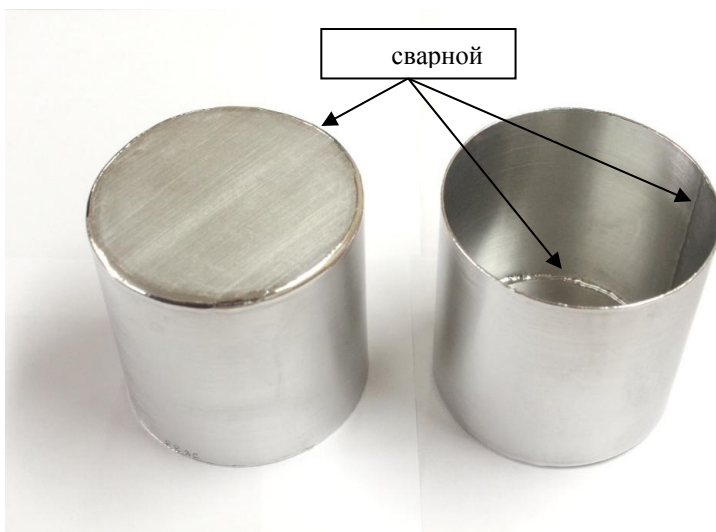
Цилиндрический сварной иридиевый тигель
